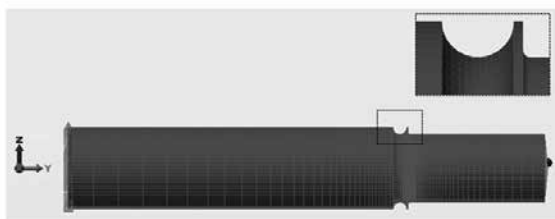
Geometría del modelo con ranura, con restricciones y carga aplicada en el extremo no empotrado
